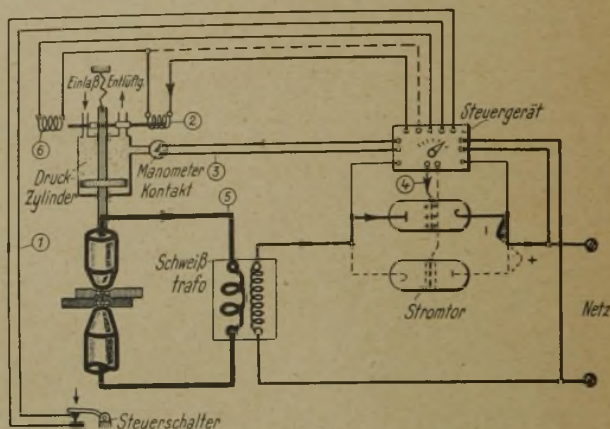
Elektrische Punktschweißung, Gittersteuerung
